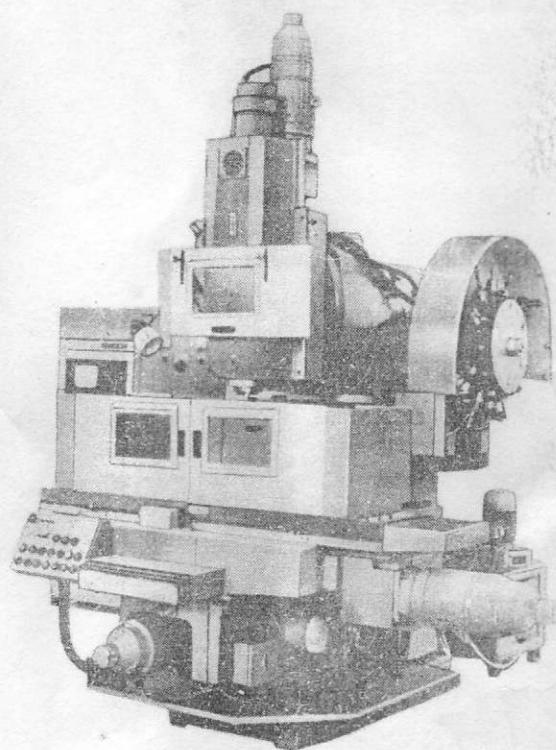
Рис. I. Станок ГФ2171 фрезерный консольный вертикальный с ЧПУ и автоматической сменой инструмента
